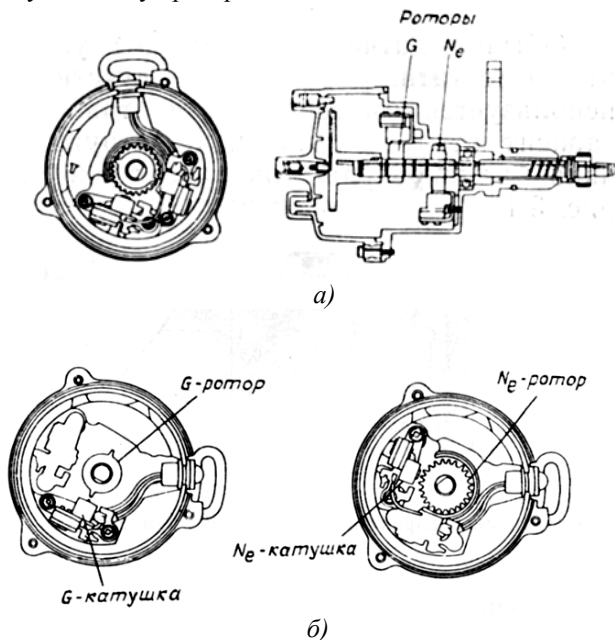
Датчик угла поворота коленчатого вала двигателя:
